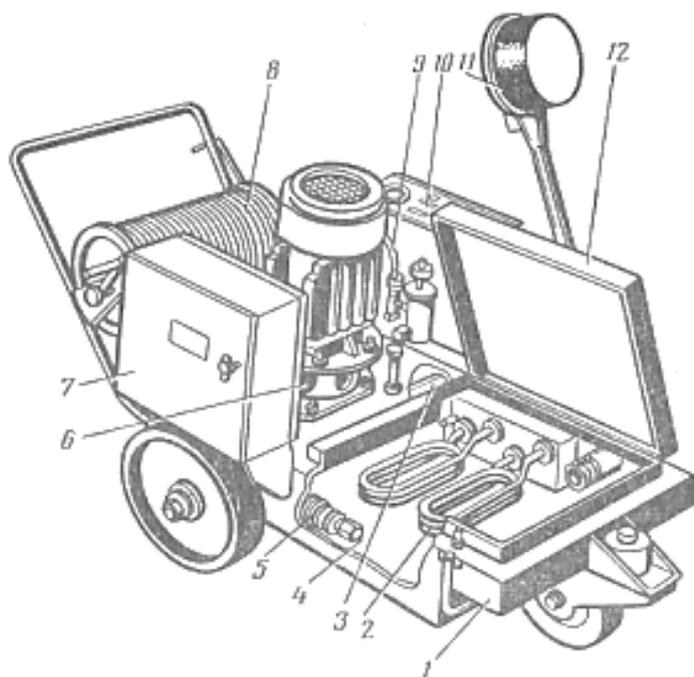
Установка ОМ-28171А для промывки смазочной системы двигателя.
